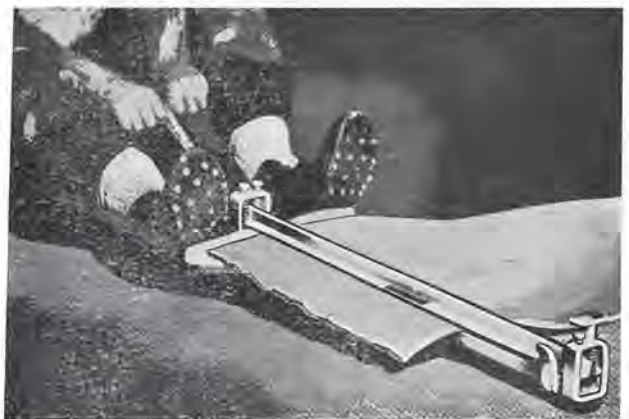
Machine «Comet» fixée sur la bande. L'ouvrier tire la poignée et réalise la coupe.
